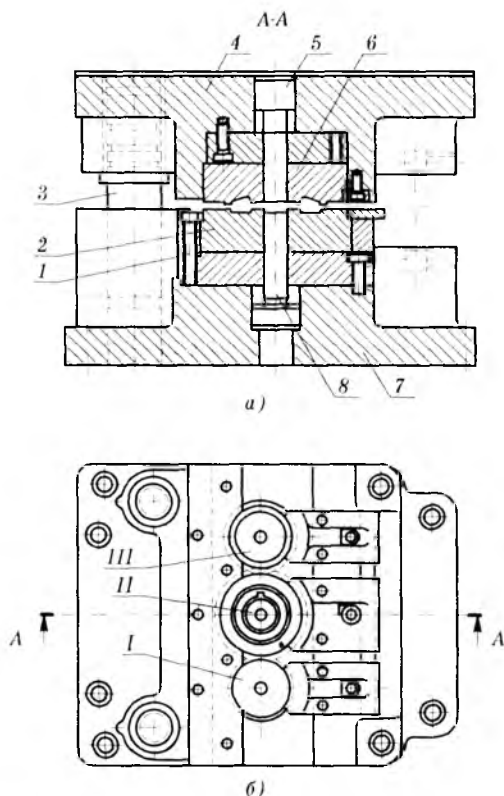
Открытый сборный штамп со вставками для штамповки в прессе:
